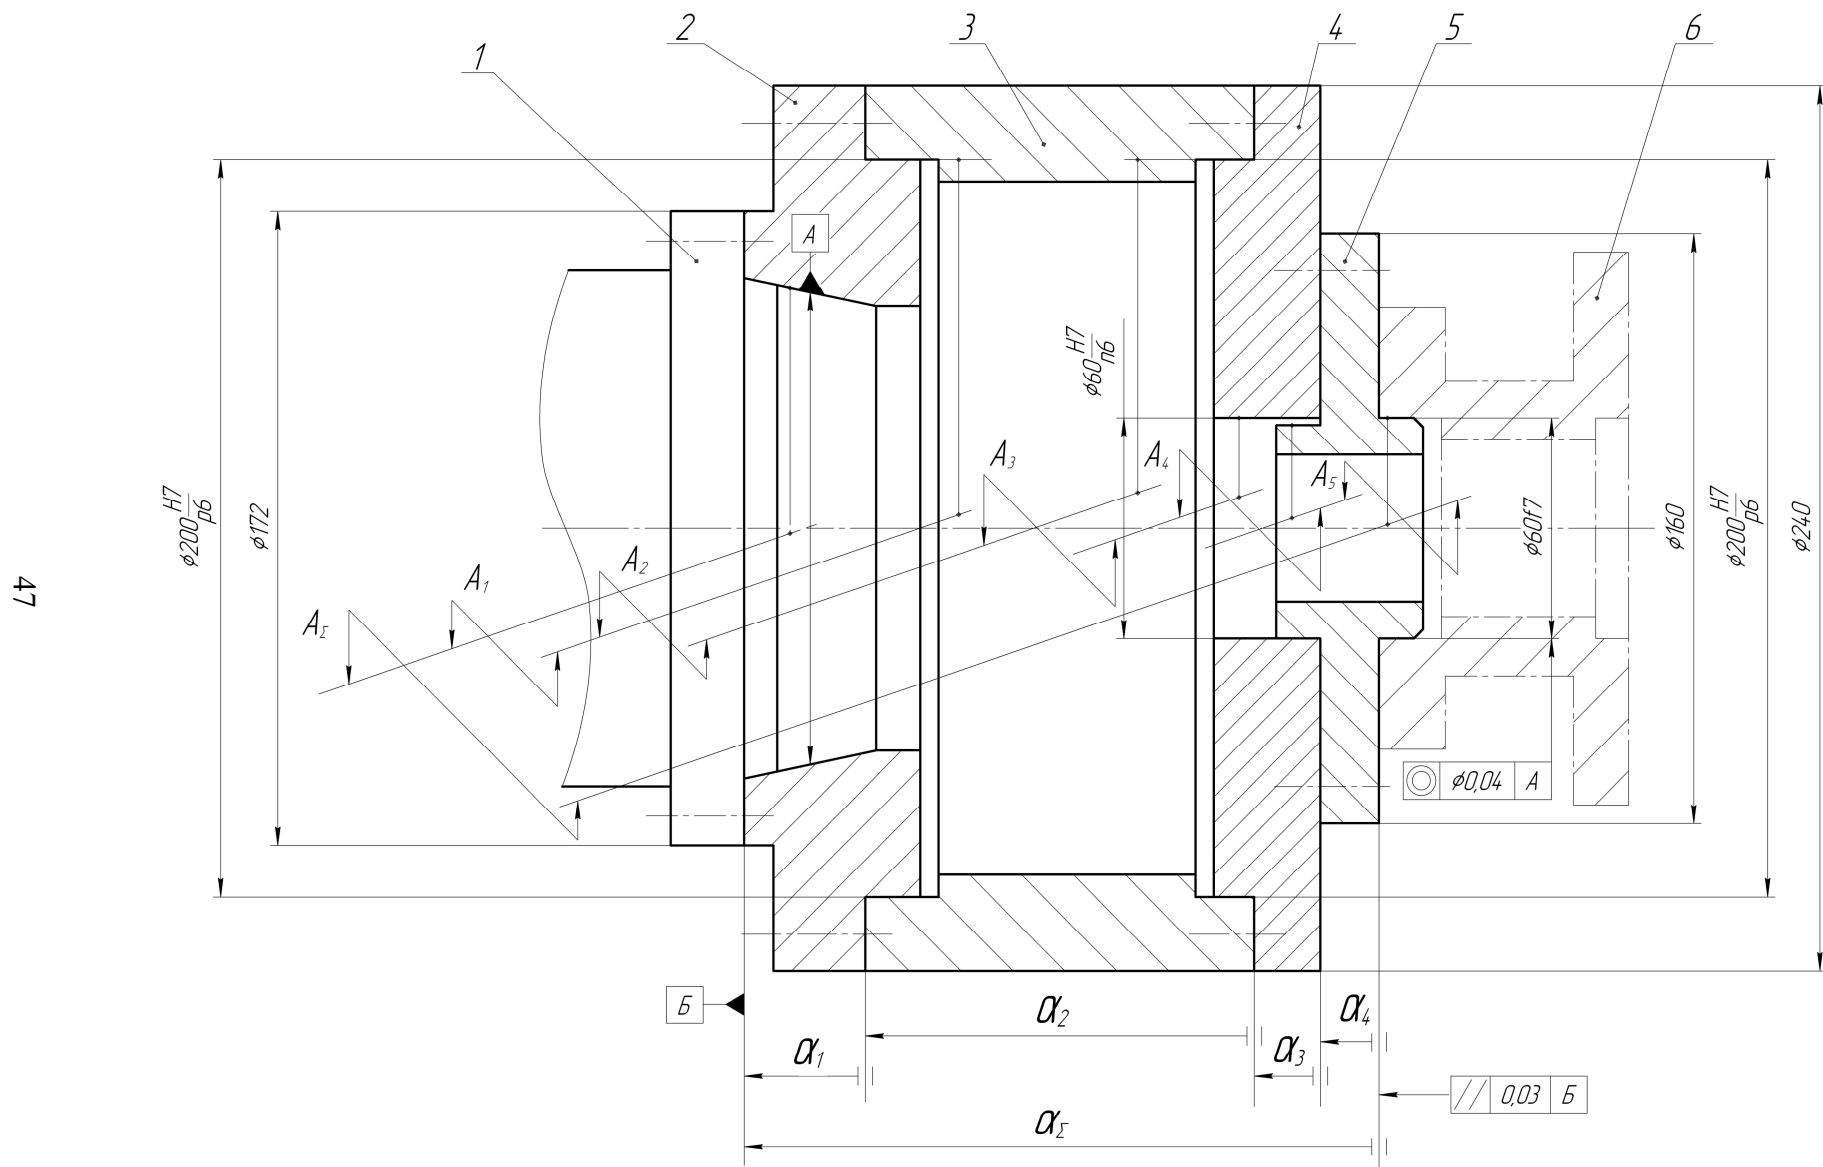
Схема токарного пристрою з розмірними ланцюгами
